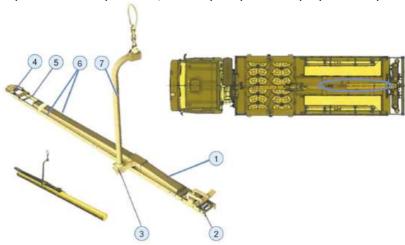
Устройство для заряжания ракет [7, с. 143]: 1- балка; 2-4- стопоры; 5- вилка; 6- направляющие; 7- подвеска
